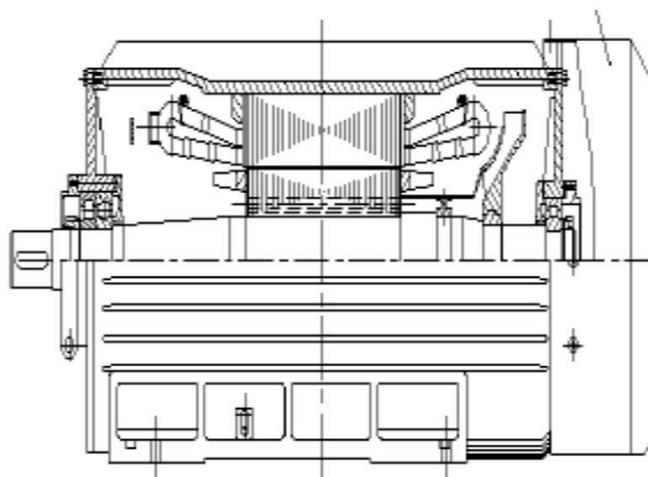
Сборочный чертеж двигателя с методом охлаждения IC416
